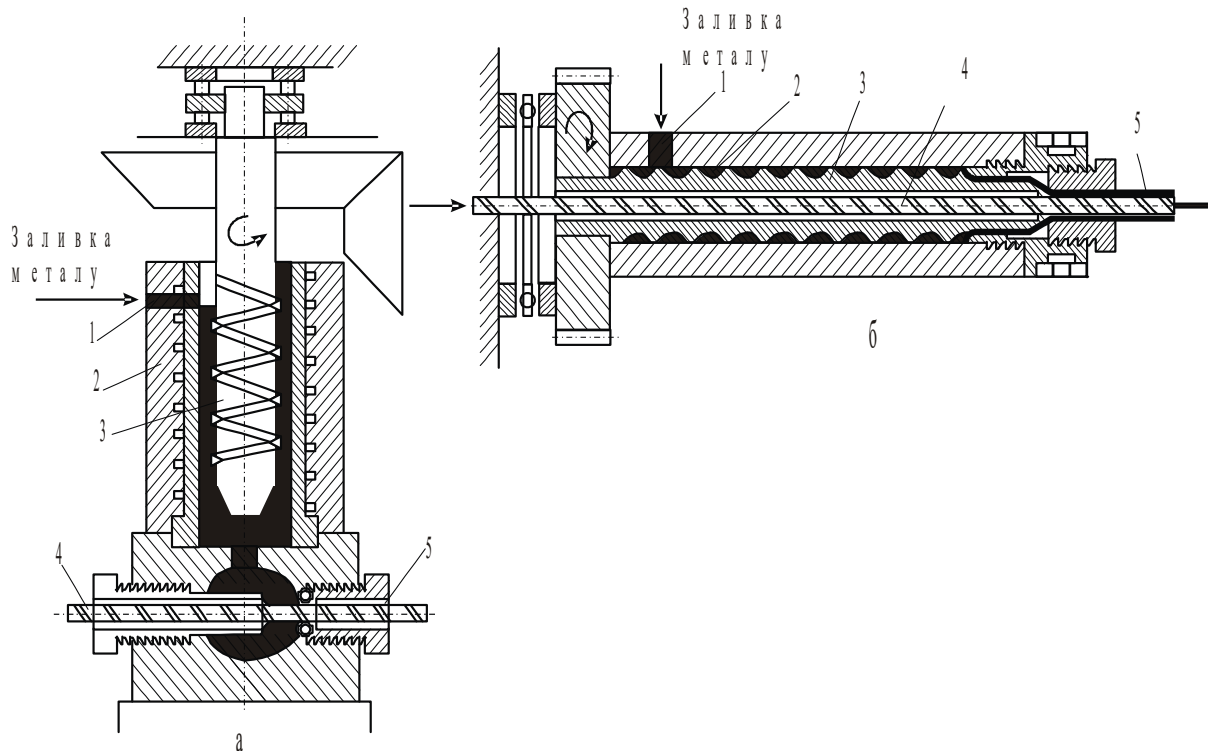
Схема накладення оболонки шляхом безперервного пресування із заливанням рідкого металу: а - прес із суцільним черв'яком; б- з порожнім черв'яком; 1 - метал для оболонки; 2 – контейнер; 3 - черв'як; 4 - кабель без оболонки; 5 – кабель із накладеною оболонкою
